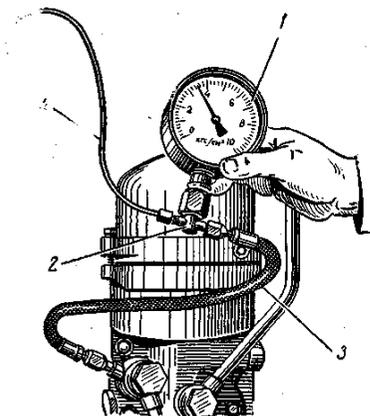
Проверка давления масла в магистрали двигателя при помощи приспособления КИ-4940:
